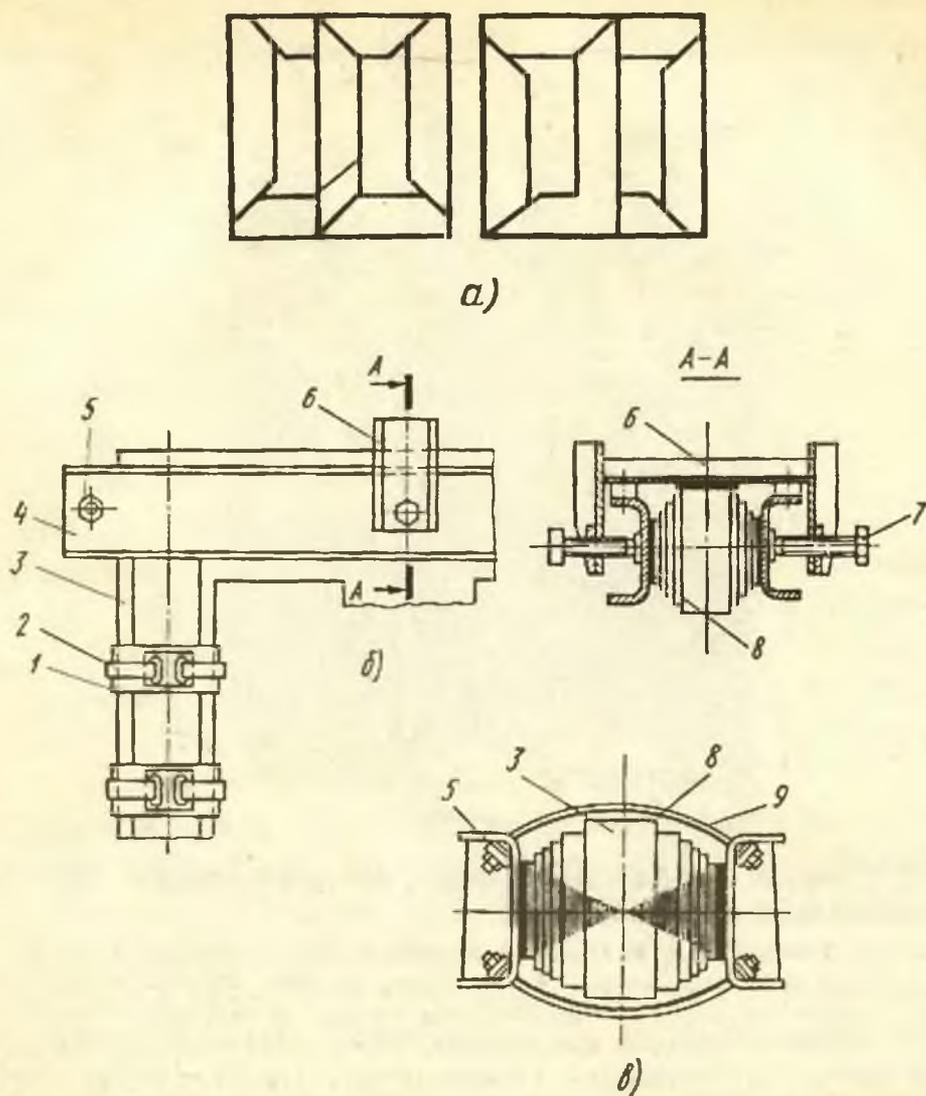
Прессовка бесшпильчатого магнитопровода трансформатора: а — схема шихтовки, б — способ прессовки ярма, в — устройство прессовки стержней; 1 — подмотка из электрокартона, 2 — стальной бандаж с пружинкой, 3 — стержень, 4 — ярмо, 5 — внешняя стяжная шпилька, 6 — прессовочная скоба, 7 — нажимной винт, 8 — электрокартонная прокладка, 9 — стальной ленточный полубандаж
